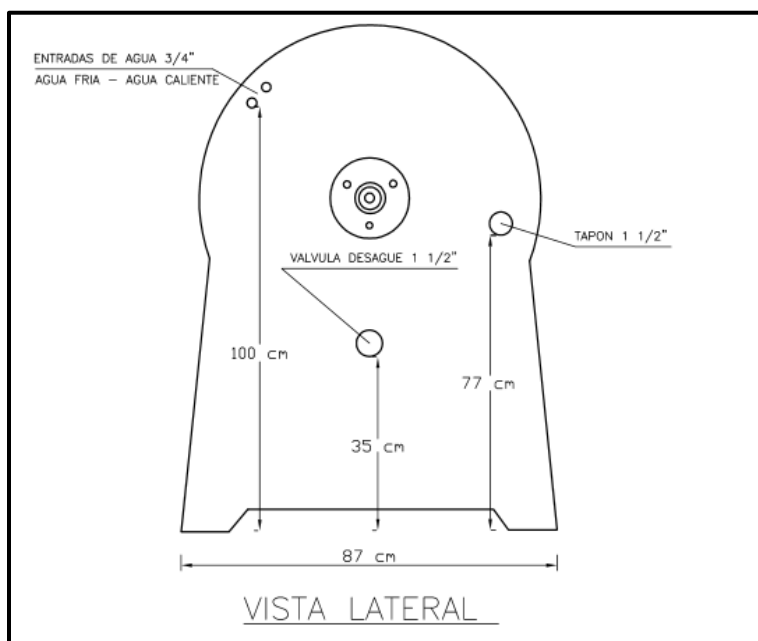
Plano lateral lavadora industrial horizontal. Nota: Autoría propia.
